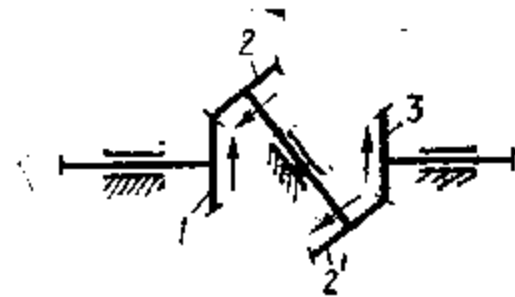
Двухступенчатый зубчатый механизм с коническими колесами
